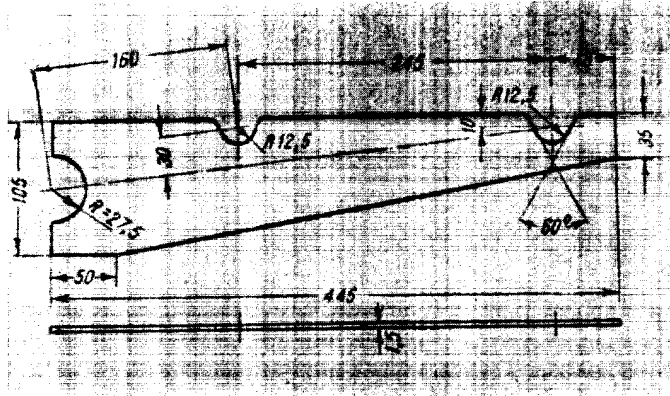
Шаблон для проверки расположения рычагов в включенном положении выключателя.
